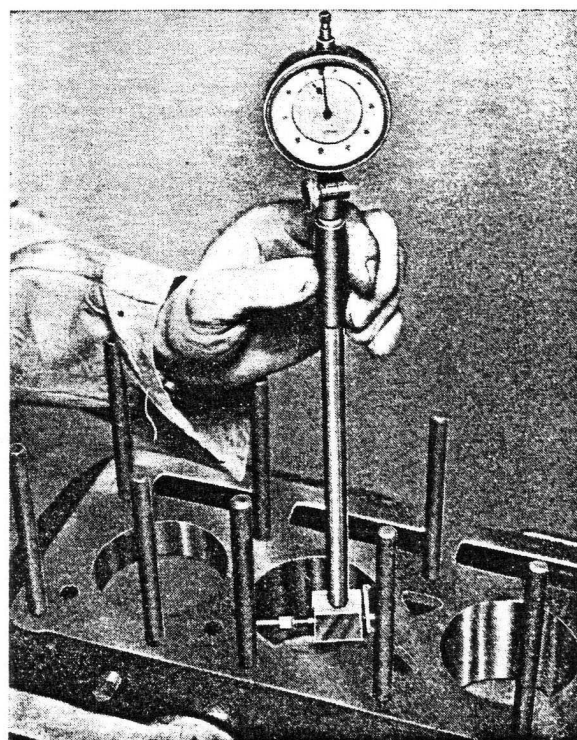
Kontrollmessung einer Zylinderbohrung
